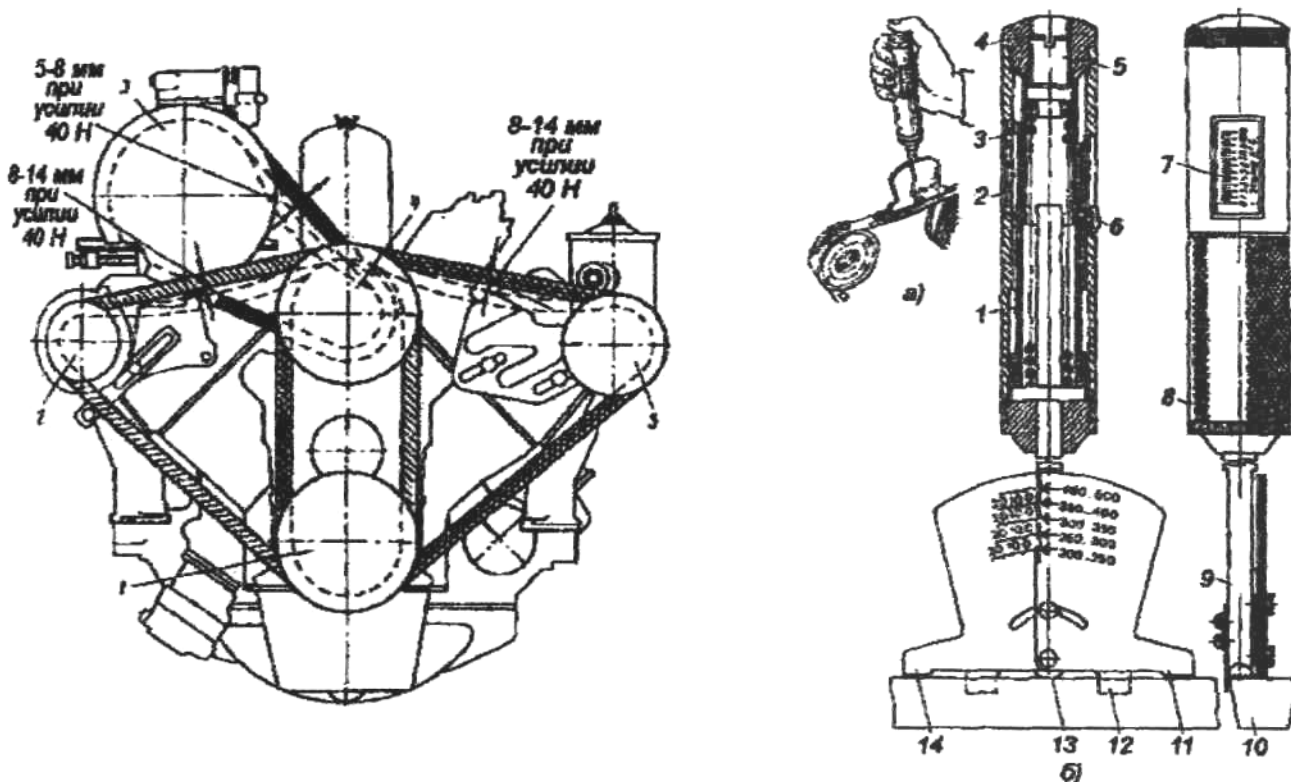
Приспособление КИ-8920 для проверки натяжения ремней: а - проверка натяжения, б - прибор
